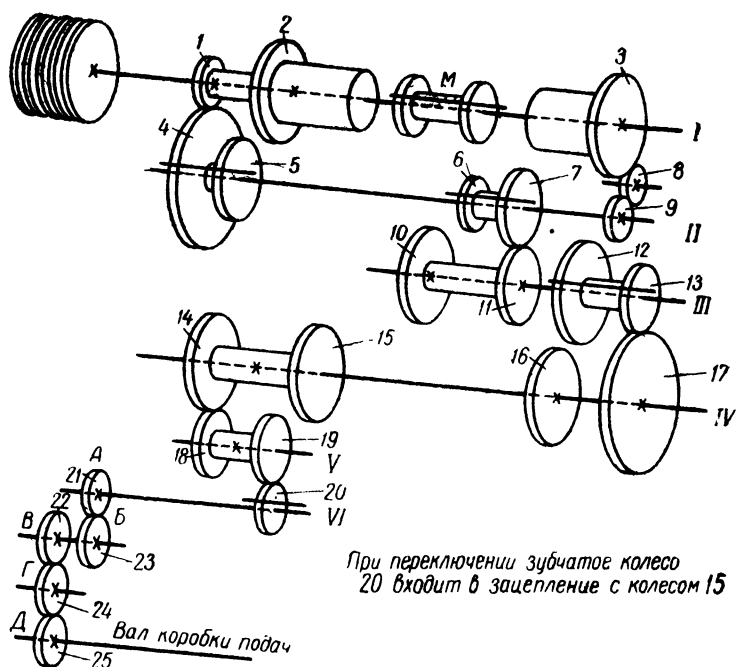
Кинематическая схема передней бабки с коробкой скоростей токарно-винторезного станка модели 1615-М.
